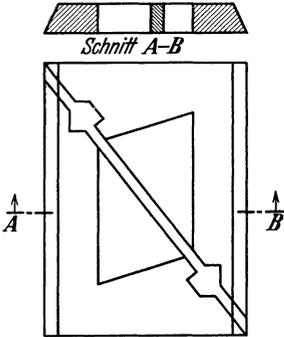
Geteilte Schnittplatte mit Mittelstege.
